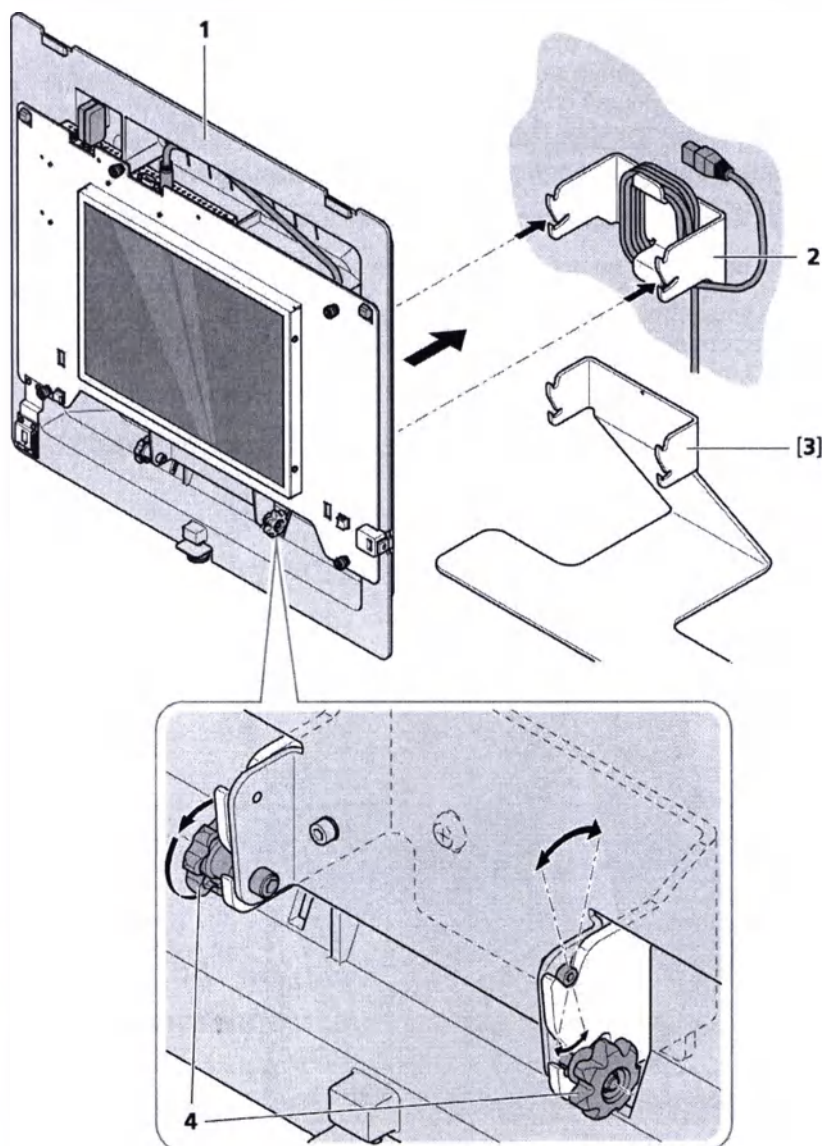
Установка корпуса прибора на кронштейн для крепления к стене или на кронштейн для установки на стол
